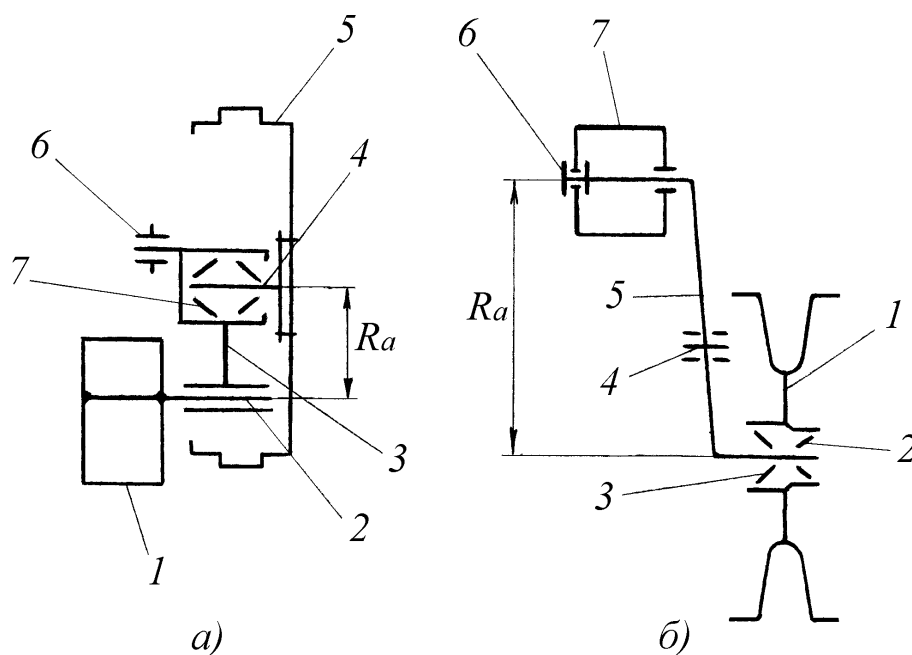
Схемы установки направляющего колеса на кривошипе
